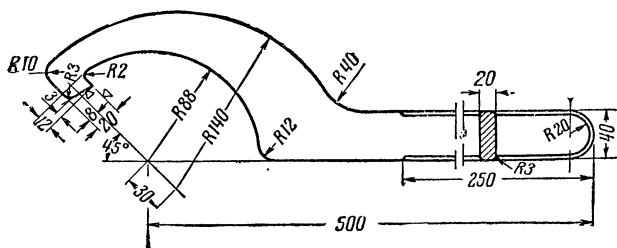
Специальный ключ для гайки ступицы ведущего колеса.
